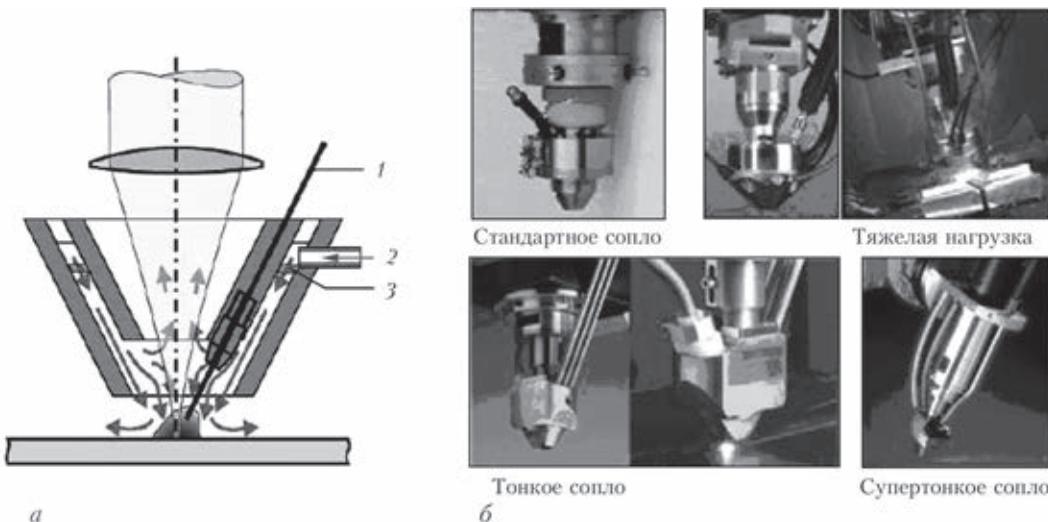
Принципиальная схема (а) и внешний вид (б) головок для гибридной лазерно-дуговой сварки с интегрированным соплом [4]: 1 — электродная проволока; 2 — вспомогательный газ; 3 — диффузионная апертура
